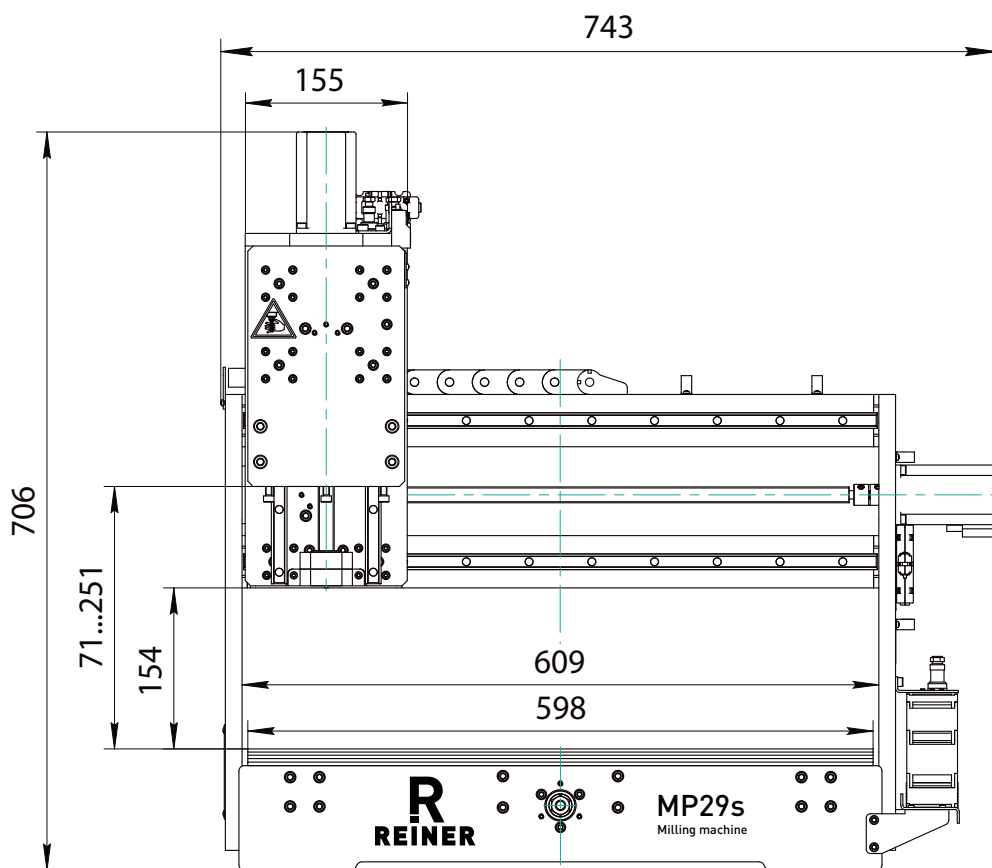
Габаритные и присоединительные размеры MP29s.
